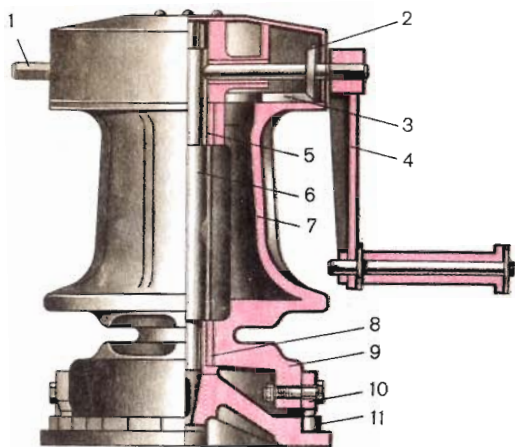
Ручной якорно-швартовый шпиль ШР4
